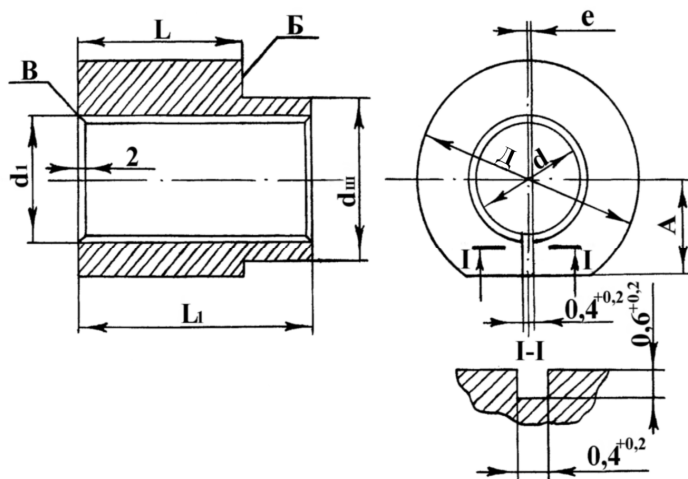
Втулка ремонтного размера насосов НШ-32УР и НШ-46УР.
